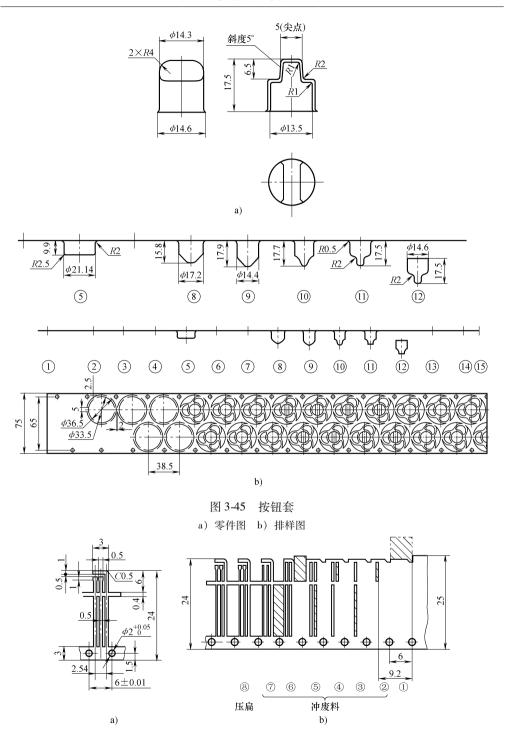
晶体管引线框 a) 零件图 b) 排样图
